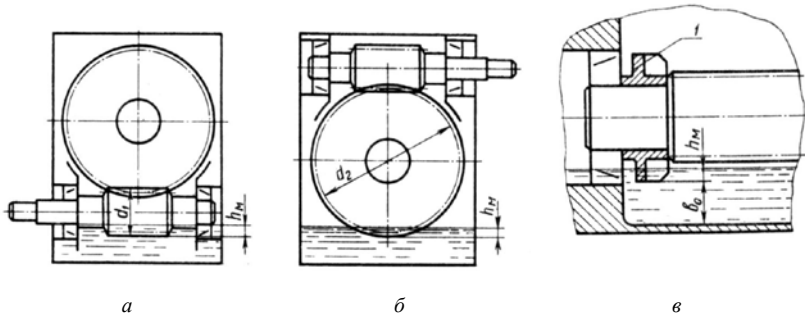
Глубина погружения в масло деталей червячного редуктора
